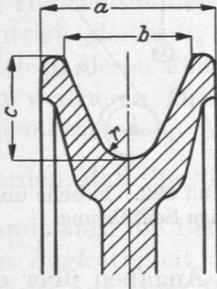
Rillenprofil für Seilrollen nach DIN 690.
